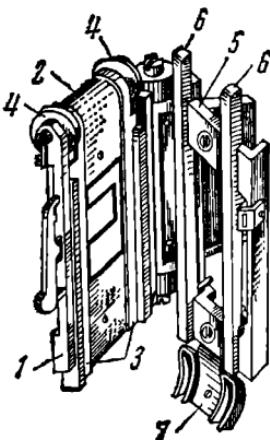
Общий вид филькового канала киноопротора типа КН: 1 — основание канала; 2 — вкладыши; 3 — рабочие поверхности; 4 — поперечно-направляющий ролик; 5 — дверца; 6 — прижимные полозки; 7 — полукруглый прижимной полозок
